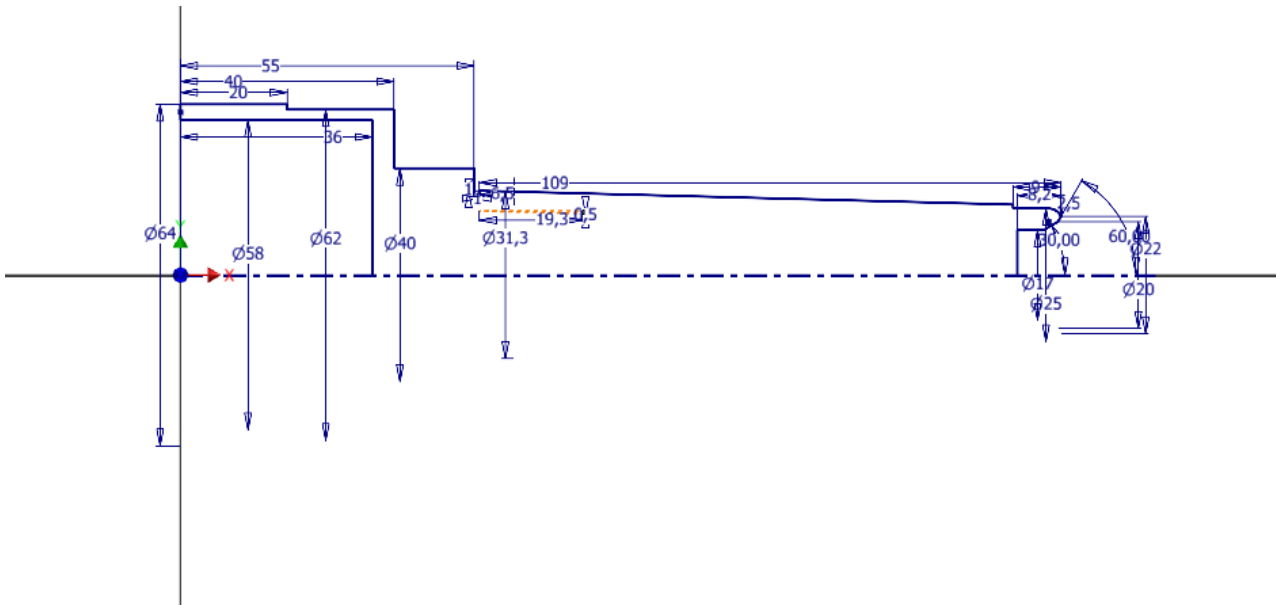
Побудова ескізу для обертання заготовки
